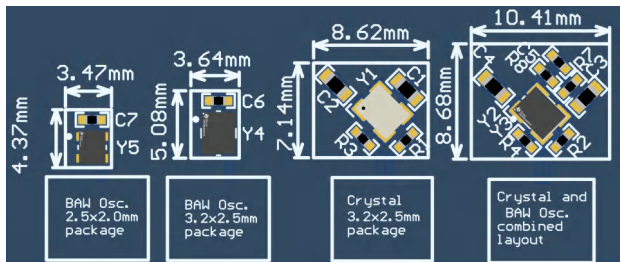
BAW와 크리스탈 오실레이터의 PCB 풋프린트 비교
